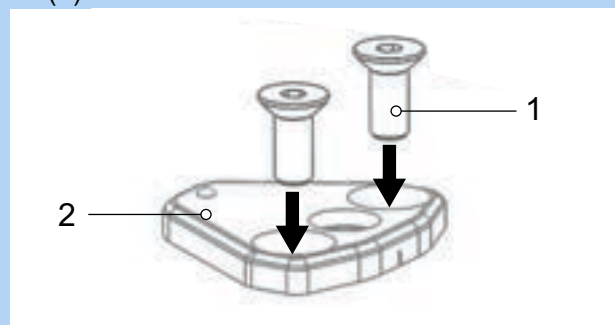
Senkkopfschrauben in Basisplatte stecken
